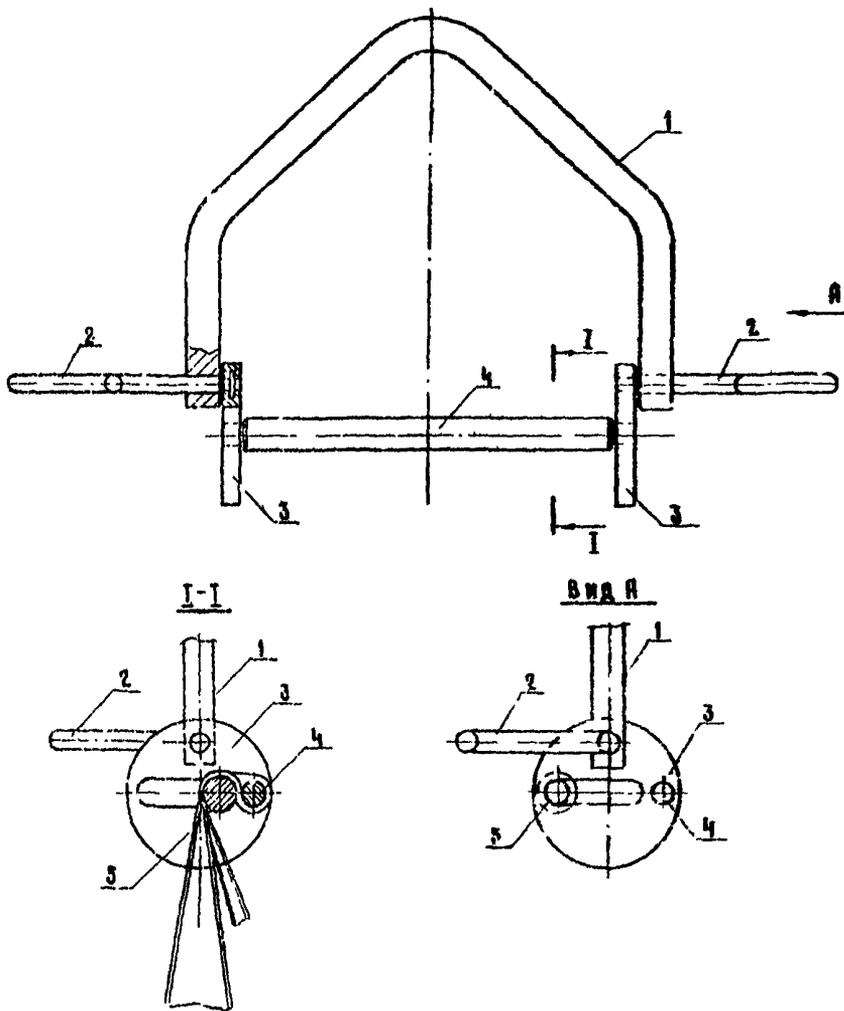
Грузоулавливающее приспособление с полусферической запорной горловиной контейнера: 1 - дуга; 2 - рукоятка; 3 - диск; 4 - выпрямляющая штанга; 5 - поперечная штанга
